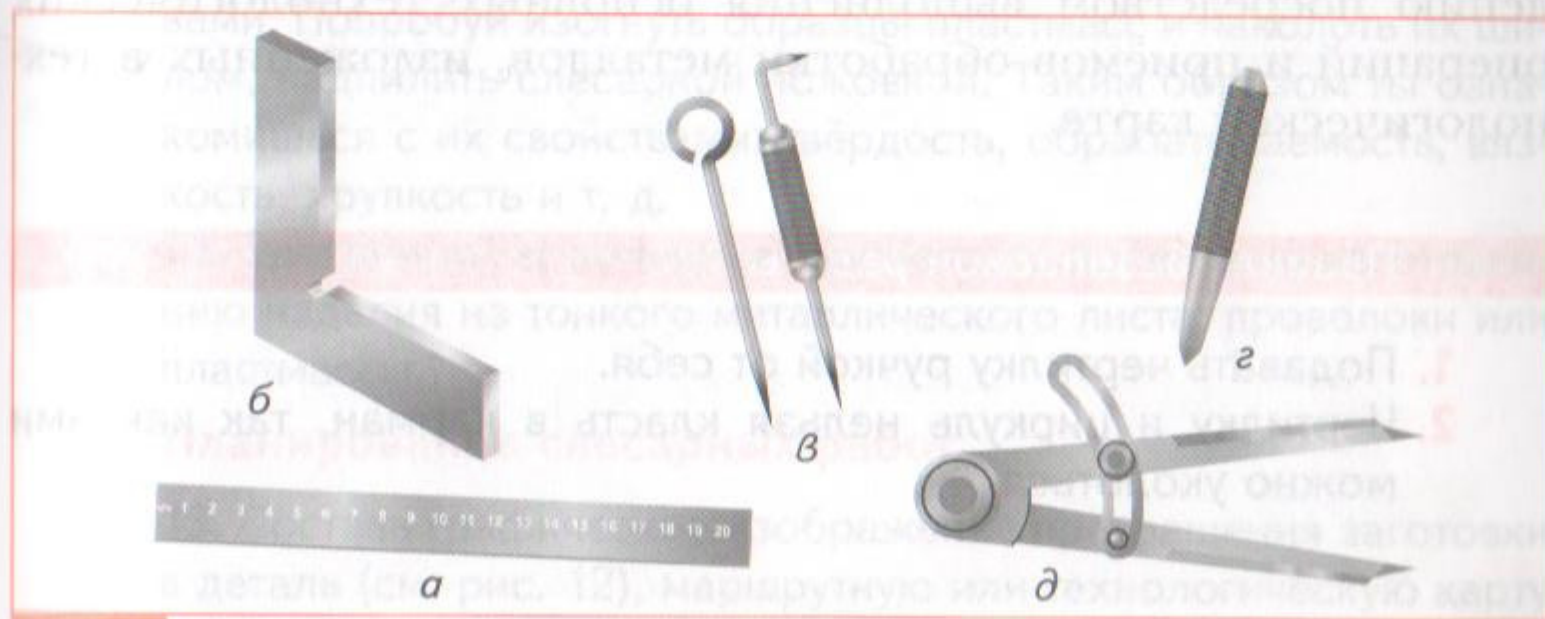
Разметочные инструменты: а — линейка; б — угольник; в — чертилка; г — кернер; д — разметочный циркуль
